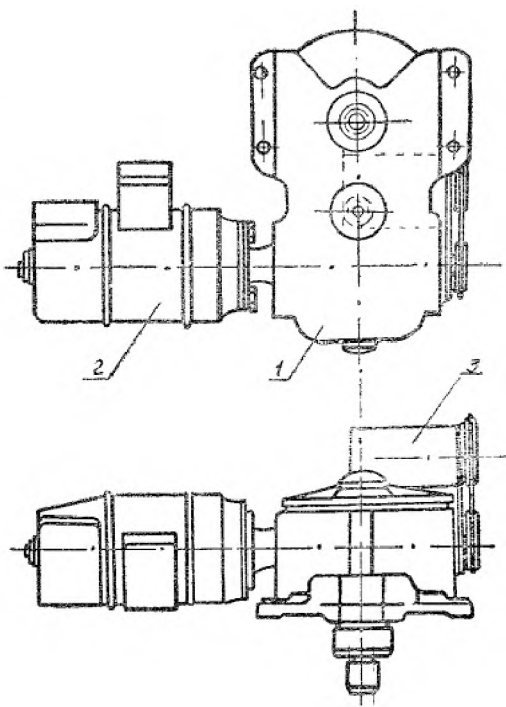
Позначення органів керування обертача зварювального М 11050А
